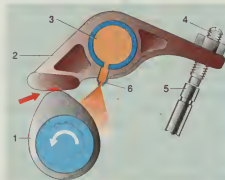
Механизм привода клапанов на двигателе XW7: 1 — распределительный вал; 2 — коромысло; 3 — ось коромысел (полюс); 4 — болт регулировки тепловоззора; 5 — клапан; 6 — форсунка подачи масла на кулачок распревала. Стрелкой показано место износа коромысла из-за дефицита смазки.
